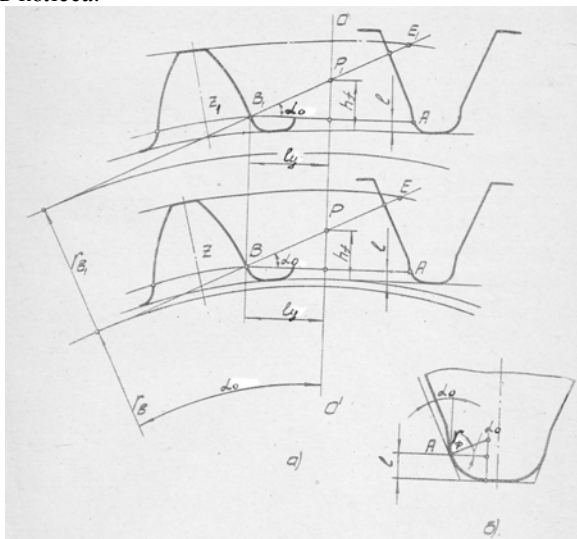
К определению установочного расстояния l_y корпусов фрезы
